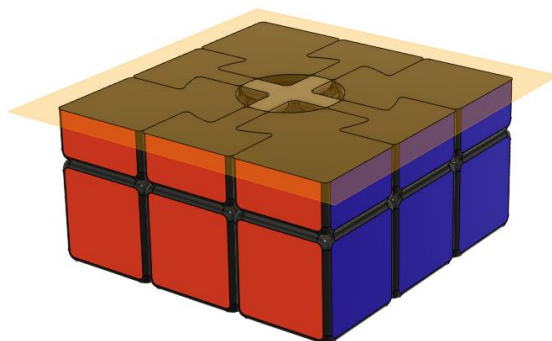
| Elaboración propia | Vista frontal del cubo con corte transversal
